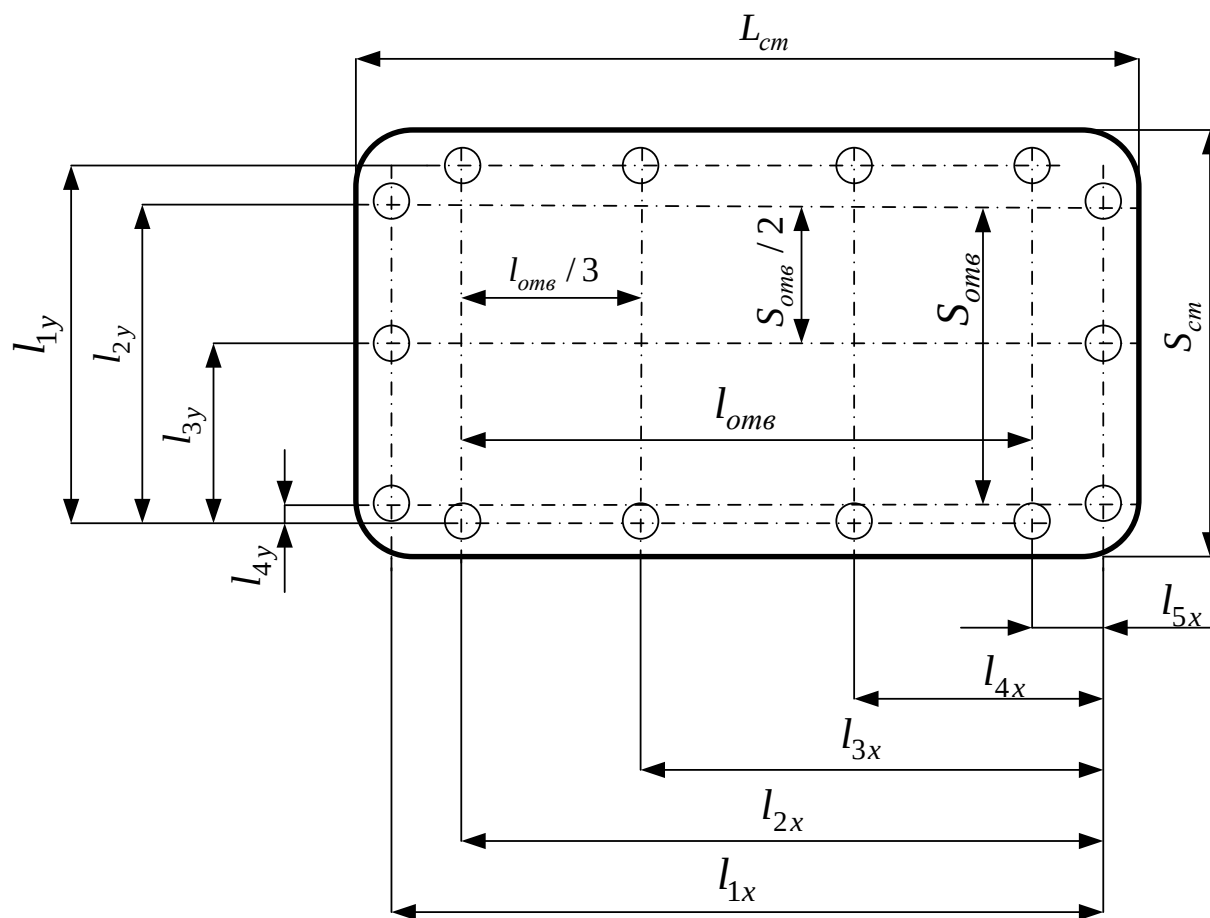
Схема расположения фундаментных болтов станка
